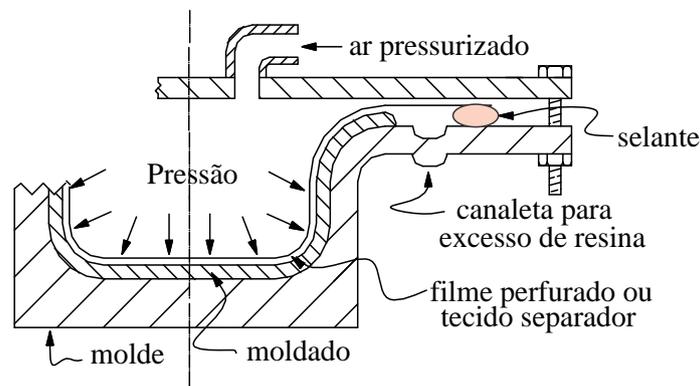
Esboço dos principais itens do processo de moldagem por membrana à pressão.
